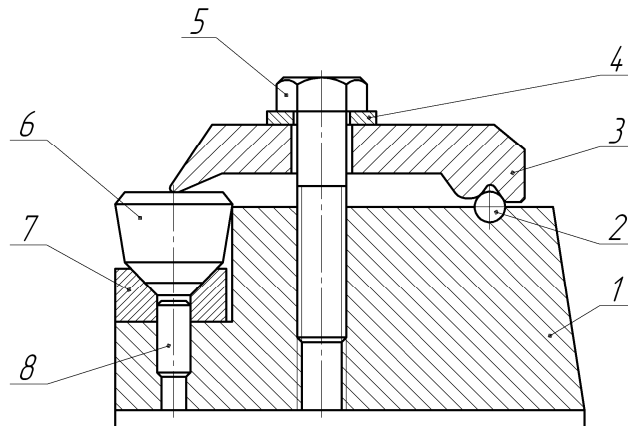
Вузол закріплення пластини з НТМ: 1 – тримач; 2 – кулька; 3 – прихват; 4 – шайба; 5 – болт; 6 – ріжуча пластина; 7 – підкладка; 8 – штифт
